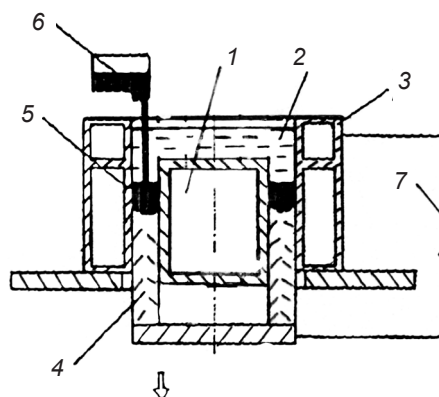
Схема процесса ЭШП ЖМ при получении полых заготовок: 1 – дорн, 2 – шлаковая ванна, 3 – токоподводящий кристаллизатор, 4 – выплавляемая заготовка, 5 – металлическая ванна, 6 – устройство для заливки жидкого металла, 7 – источник питания
